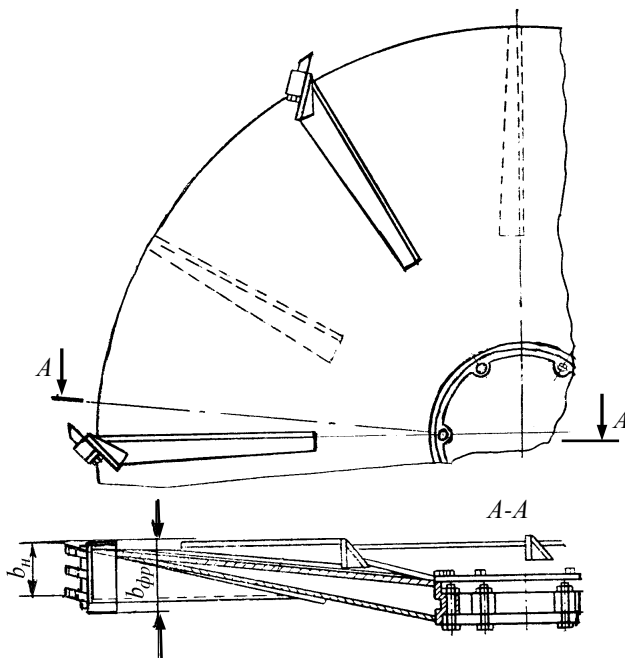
Конструкция фрезы с гребенчатыми ножами
